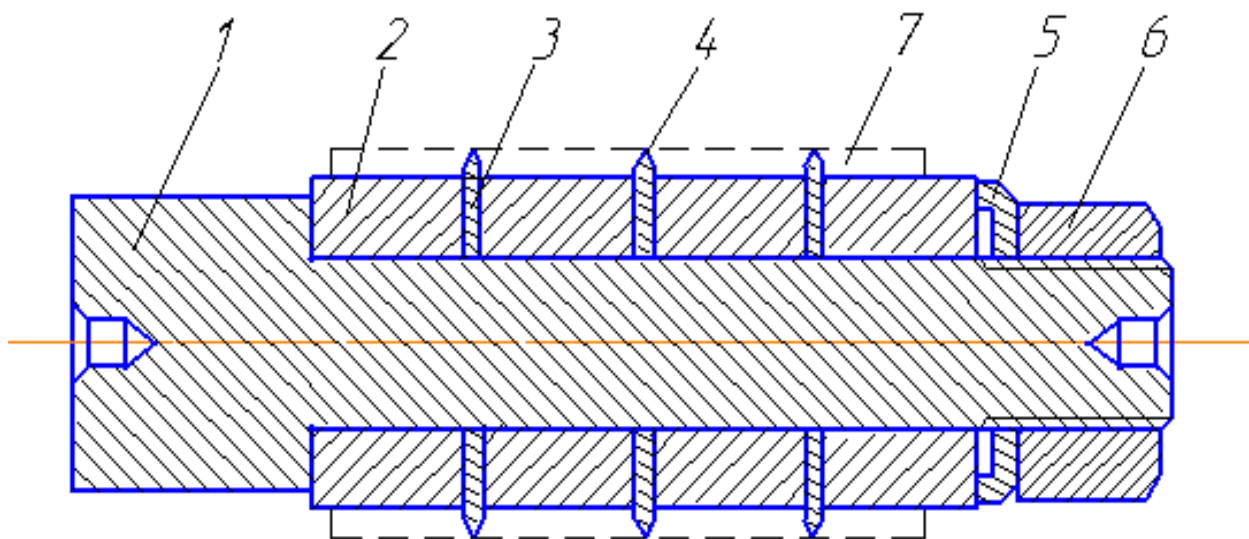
Разборное приспособление для крепления образцов при наплавке:
